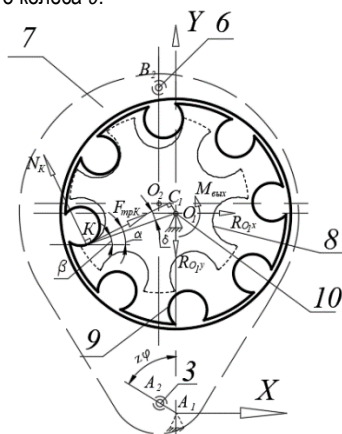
Схема действия сил на зубчатое колесо эксцентриковой передачи с параллельным расположением входного и выходного валов
